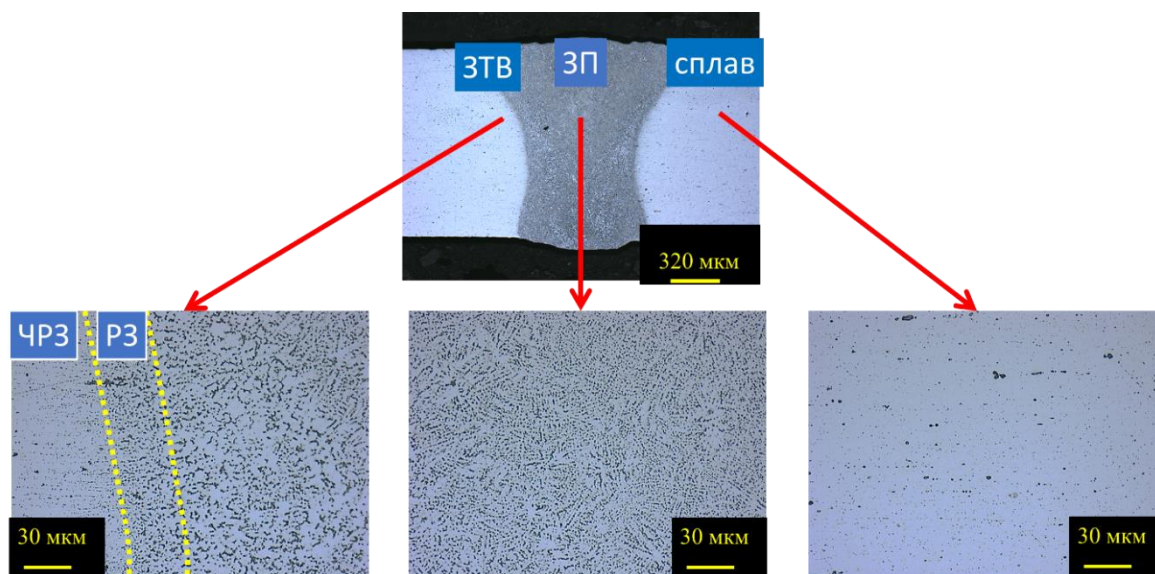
Общий вид и микроструктура поперечного сечения сварного шва и сплава 1420 системы Al-5.2Mg-2.1Li
